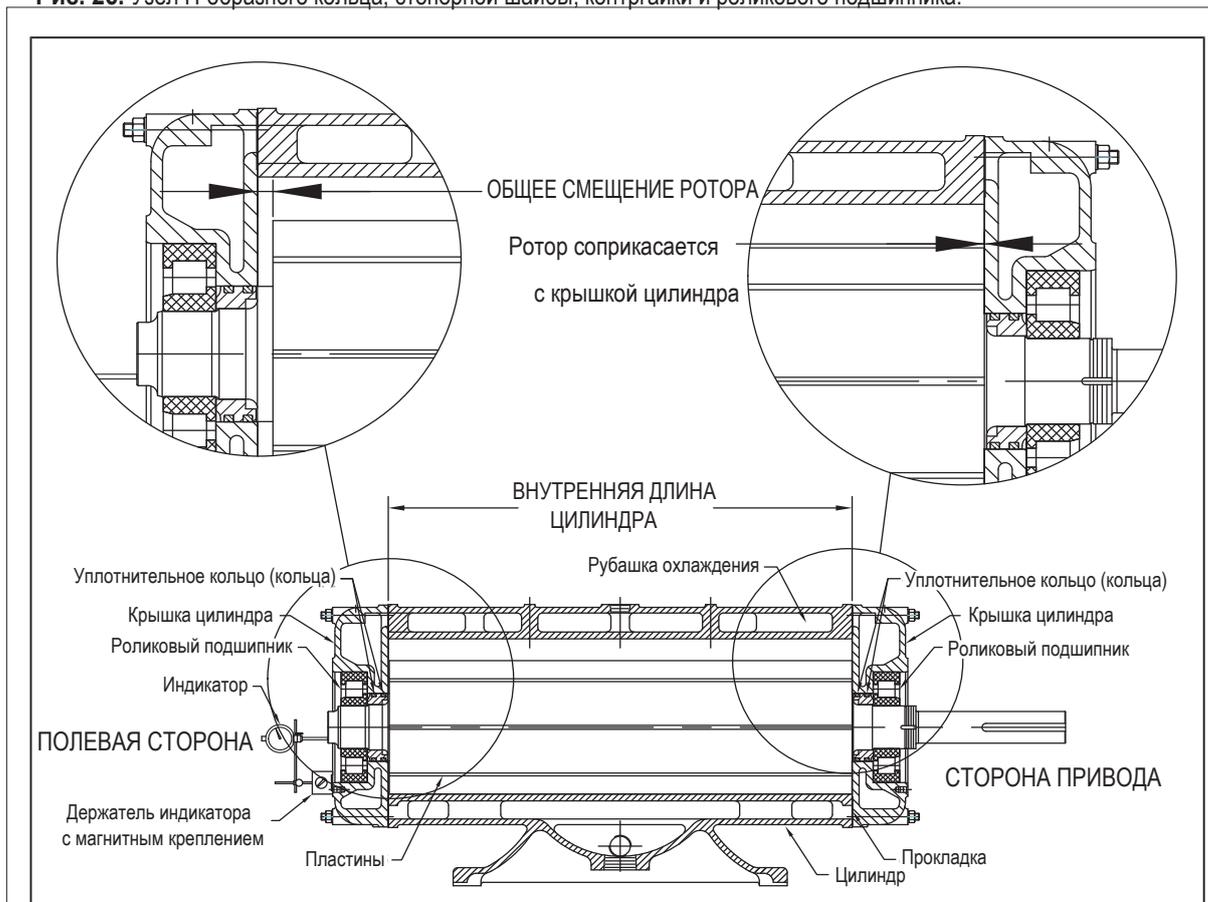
Общее смещение ротора. Подшипники не установлены на прокладки или торцевую крышку / опорную деталь уплотнения.
